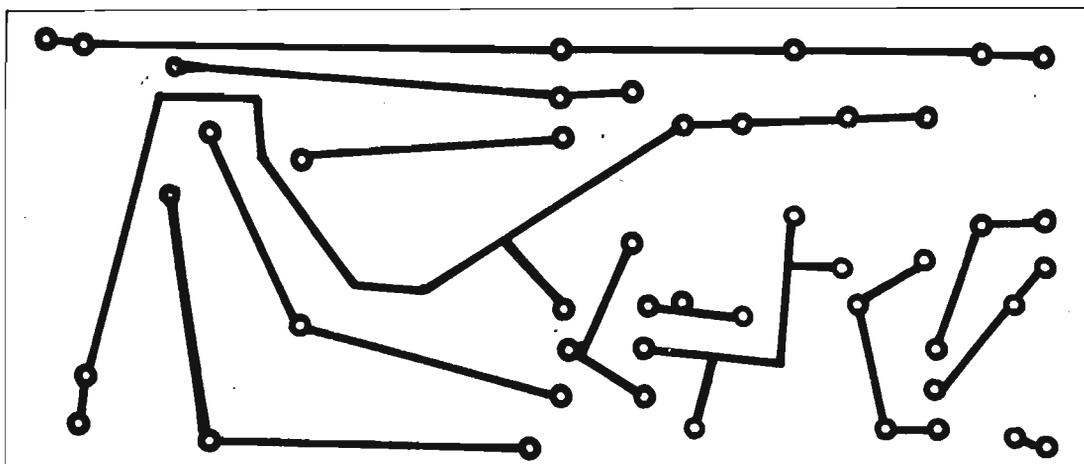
Questo disegno riproduce il circuito stampato necessario per la realizzazione del cablaggio del Signal Tracer. Il lettore dovrà riprodurlo nelle stesse dimensioni con cui esso risulta qui rappresentato.
